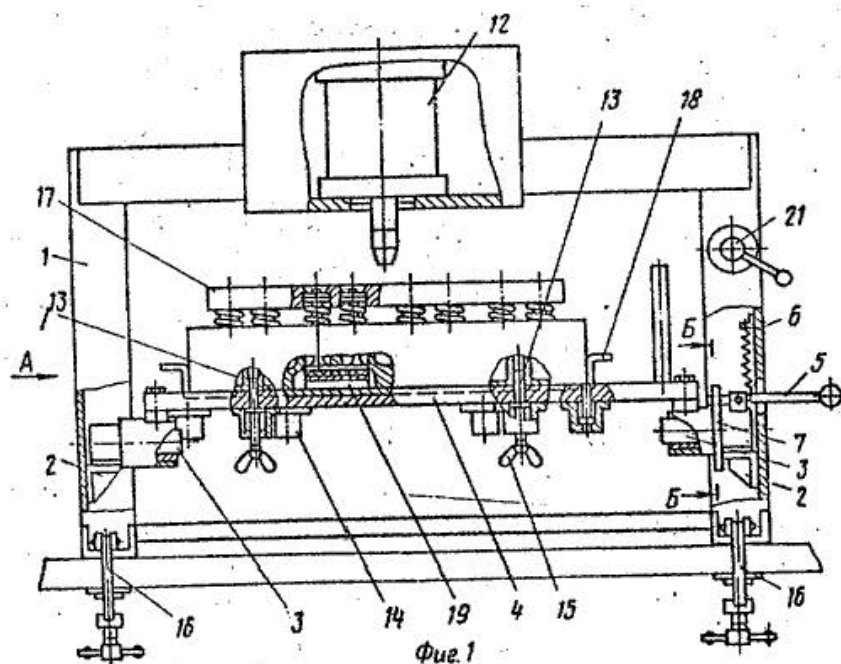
Стенд для разборки и сборки блоков цилиндров двигателей
